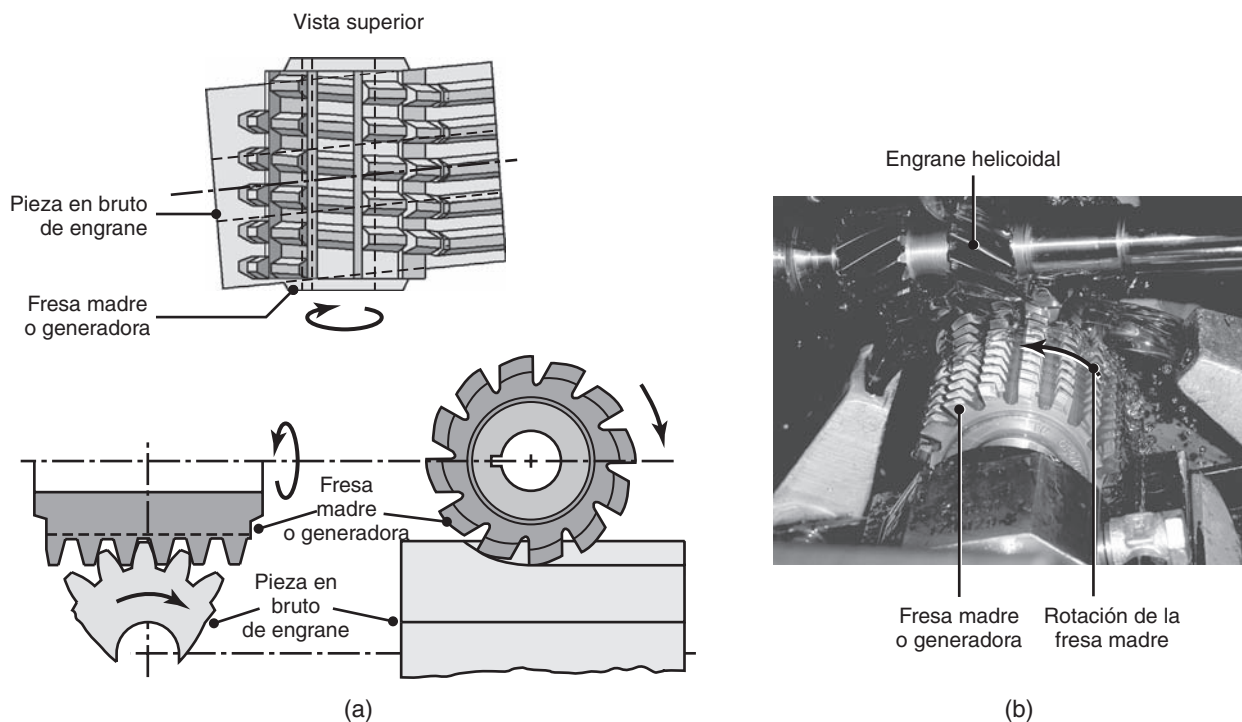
(a) Esquema de corte de engranes con una fresa madre o generadora. (b) Producción de engranes sinfín con una fresa madre o generadora. Fuente: Cortesía de Schafer Gear Works, Inc.
